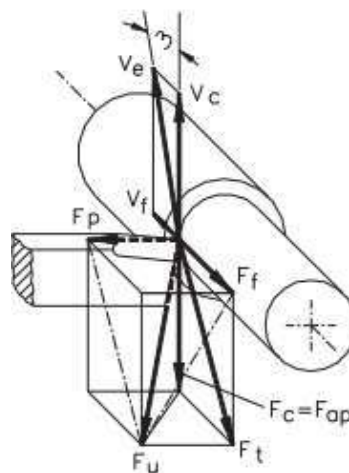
Componentes das forças de usinagem no processo de torneamento.
